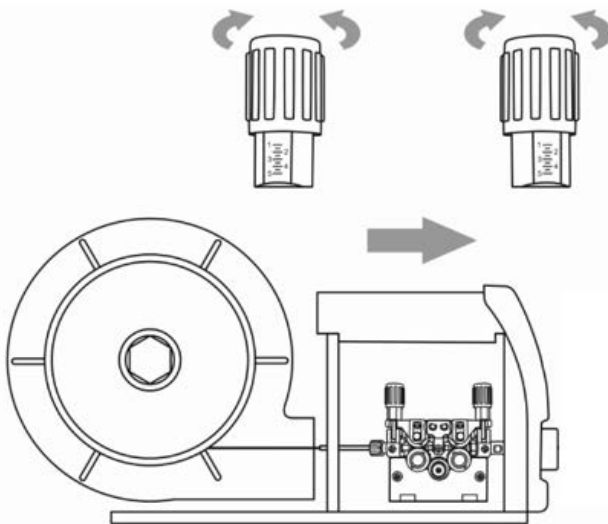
Усилие зажатия сварочной проволоки.
